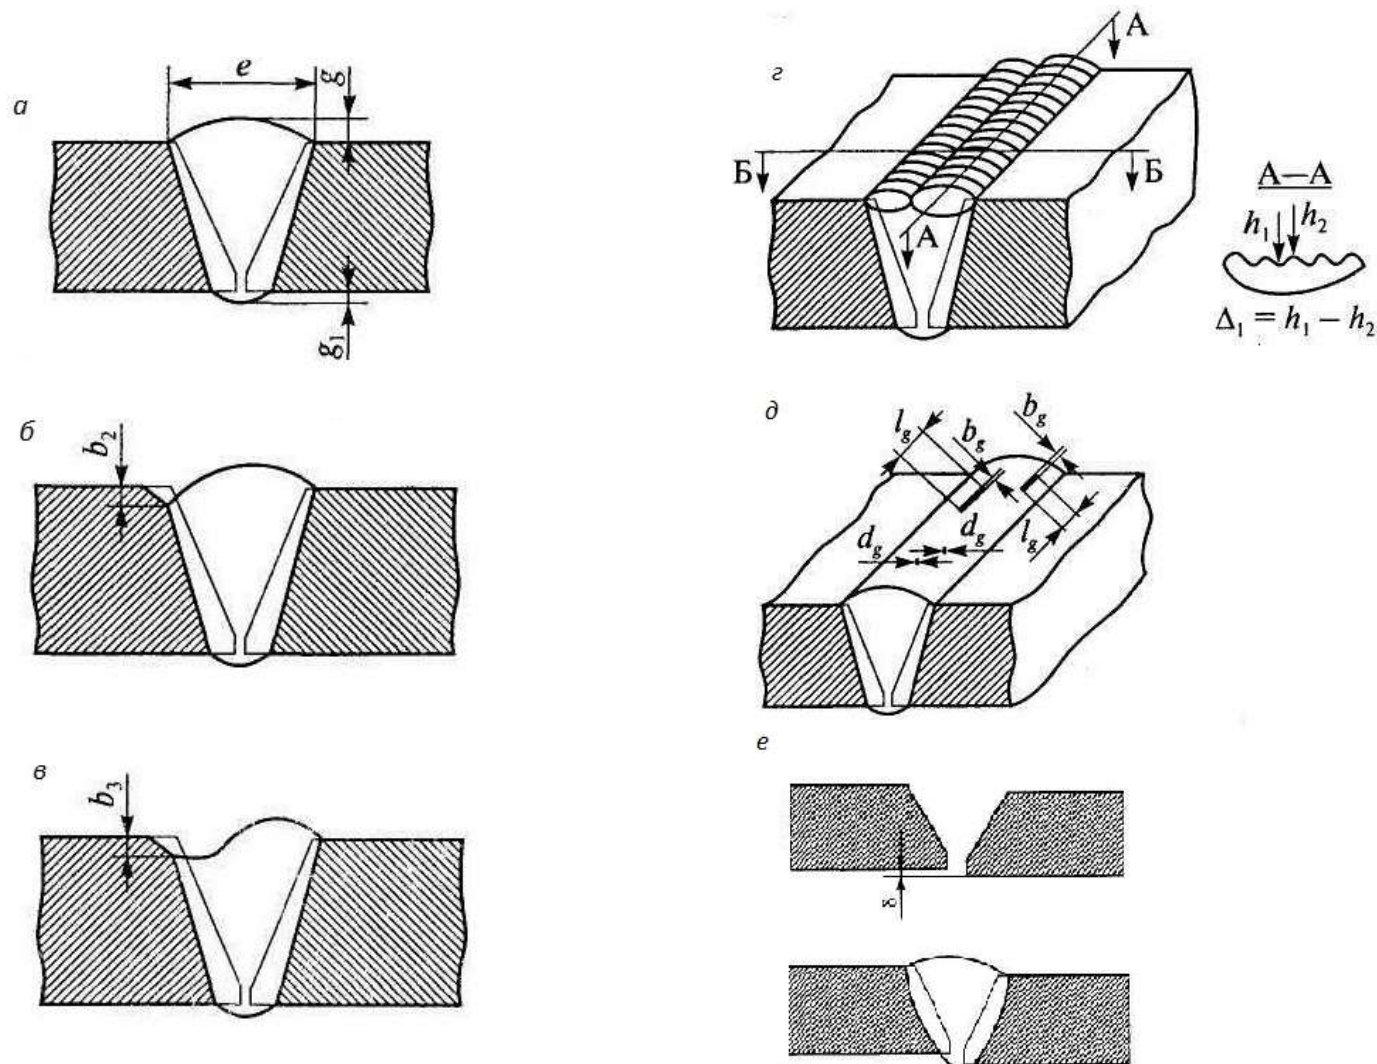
Конструктивные элементы и дефекты сварного шва, подлежащие измерительному контролю
